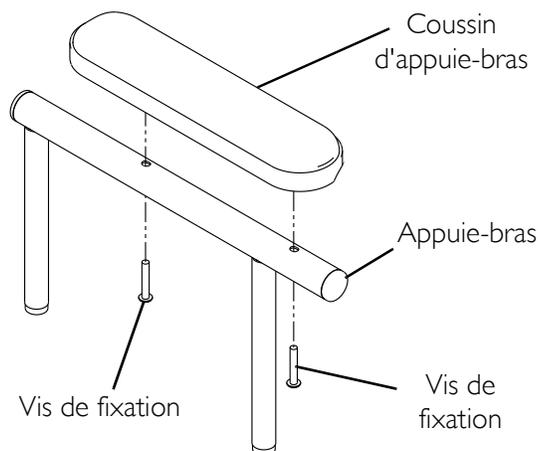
Remplacement de la manchette des appuis-bras réglables en hauteur conventionnels
